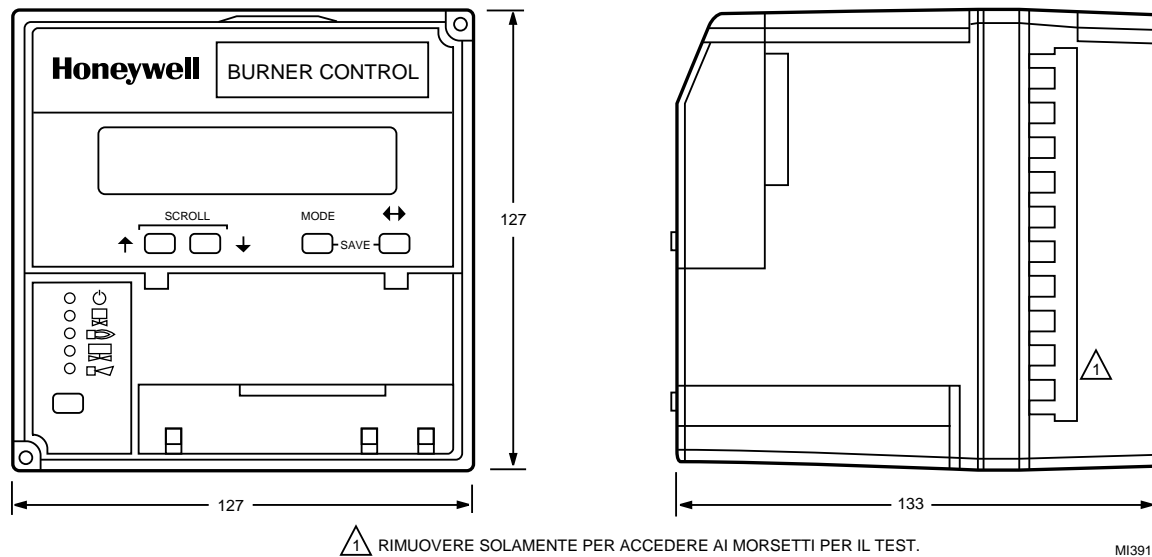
Dimensioni in millimetri per il montaggio del modulo a relè e della sottobase Q7800A.
